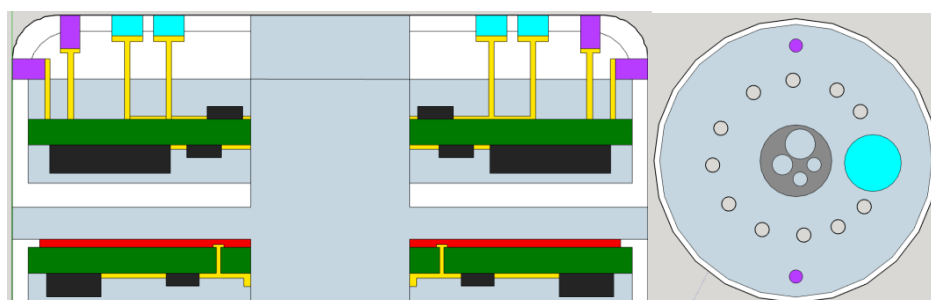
Distribución de componentes relevantes en el cabezal (1) sección de perfil (2) planta
